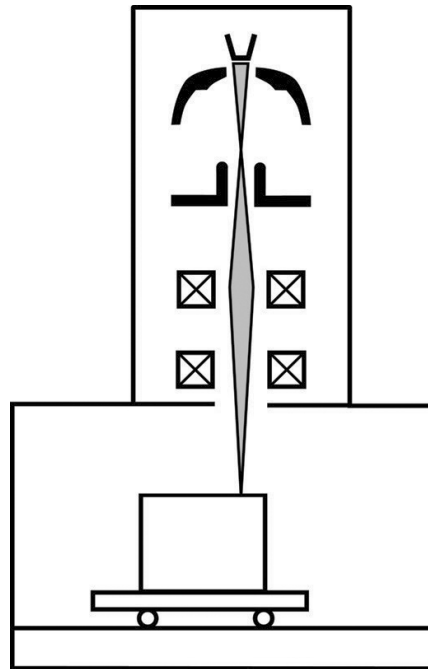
Schéma de principe du soudage par faisceau d'électrons.
